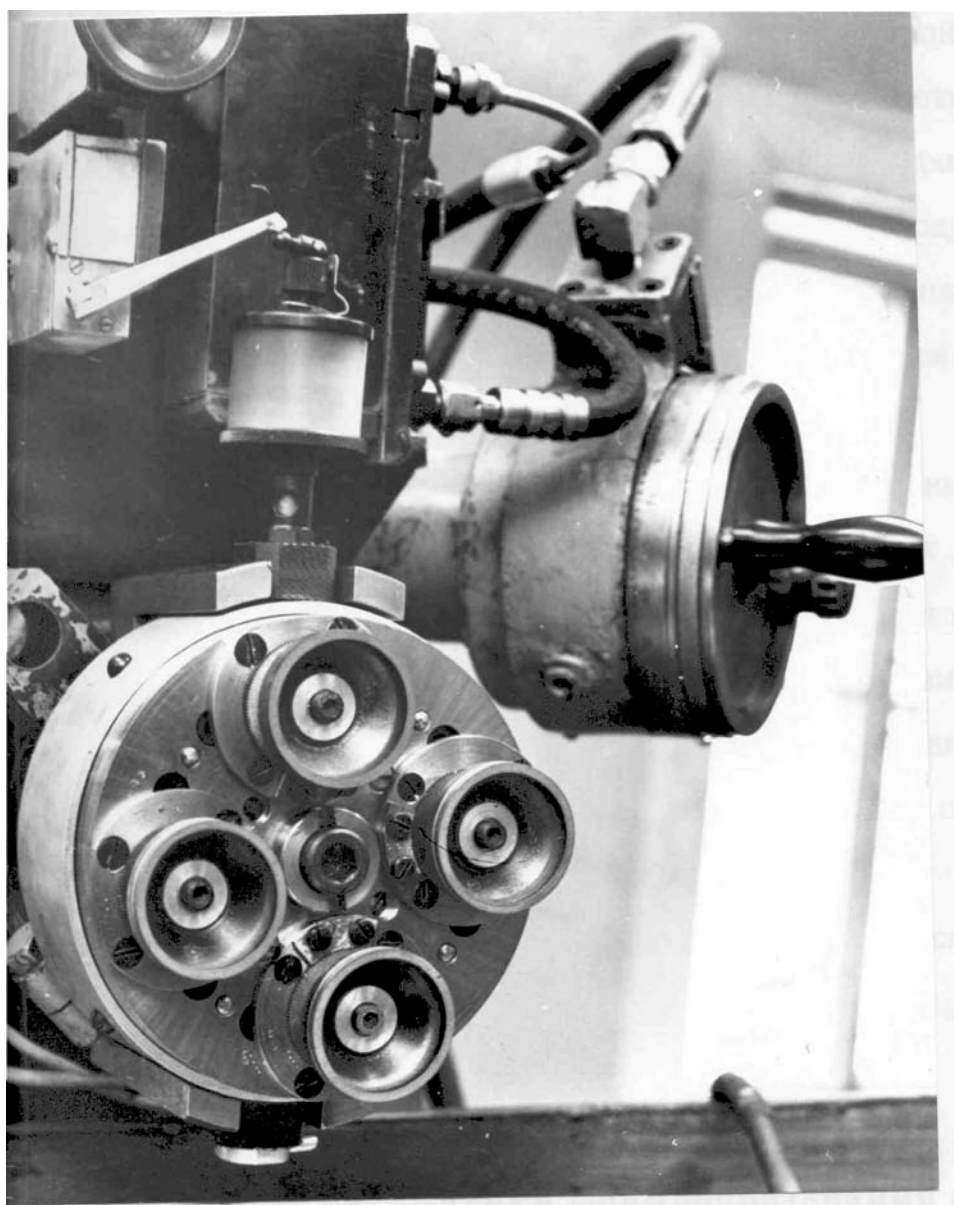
установка планетарной головки на плоскошлифовальный станок 3Г71
